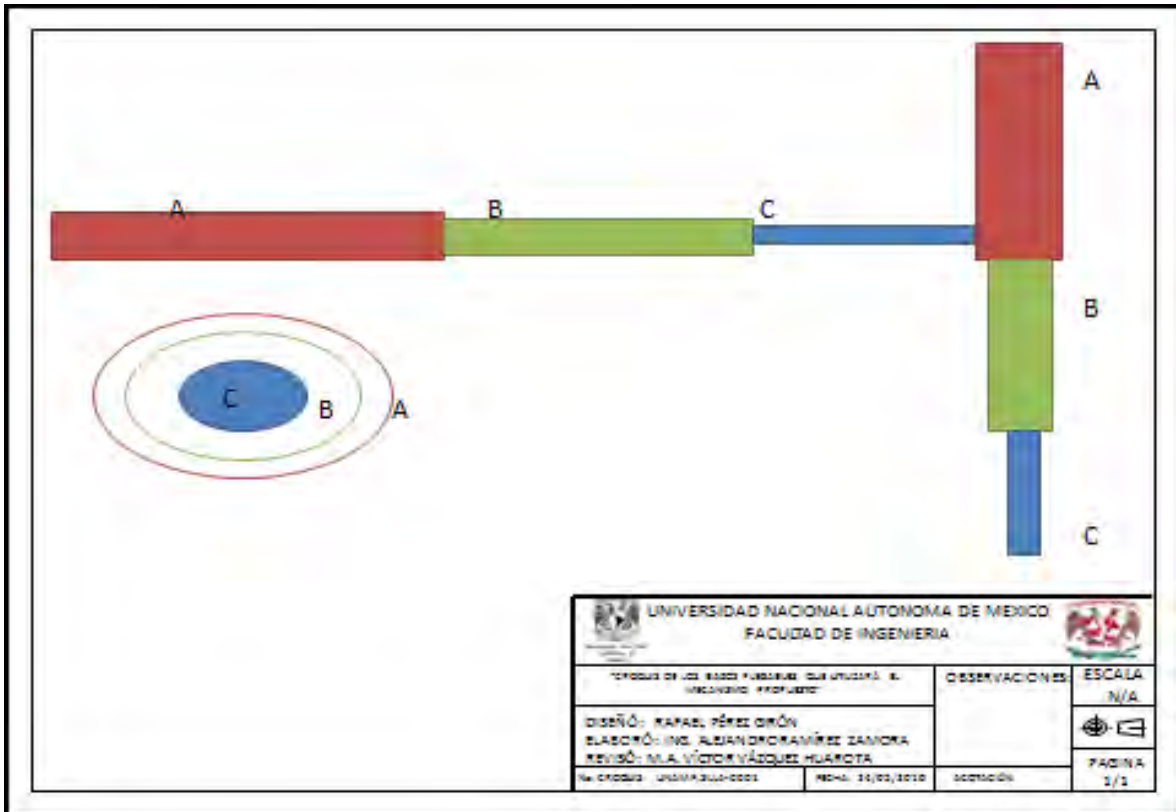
Croquis de los bazos plegables que utilizará el mecanismo propuesto
